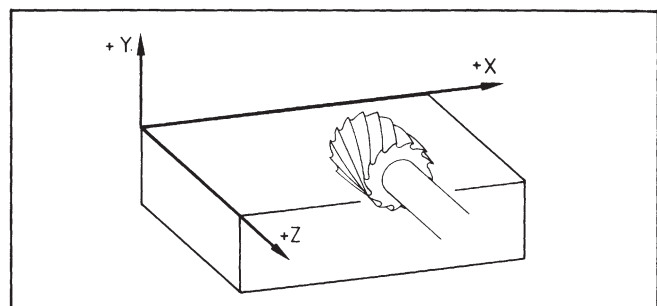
Fräsbearbeitung mit einer Universal-Werkzeugfräsmaschine
